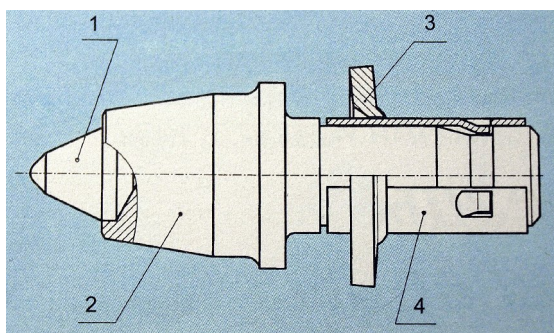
Общий вид дорожного резца СВР в сборе, изготавливаемого в ИСМ НАН Украины
